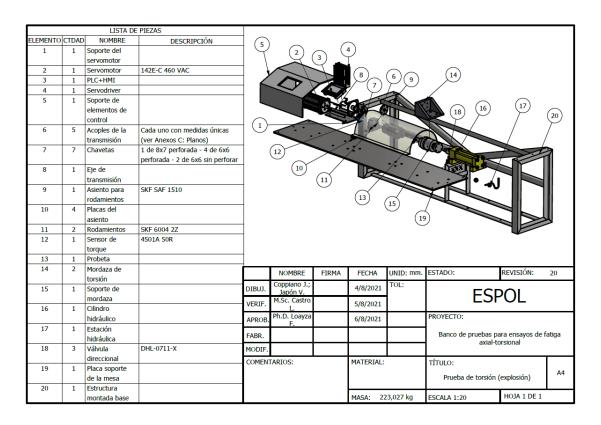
Explosión y listado de elementos para fatiga de torsión
